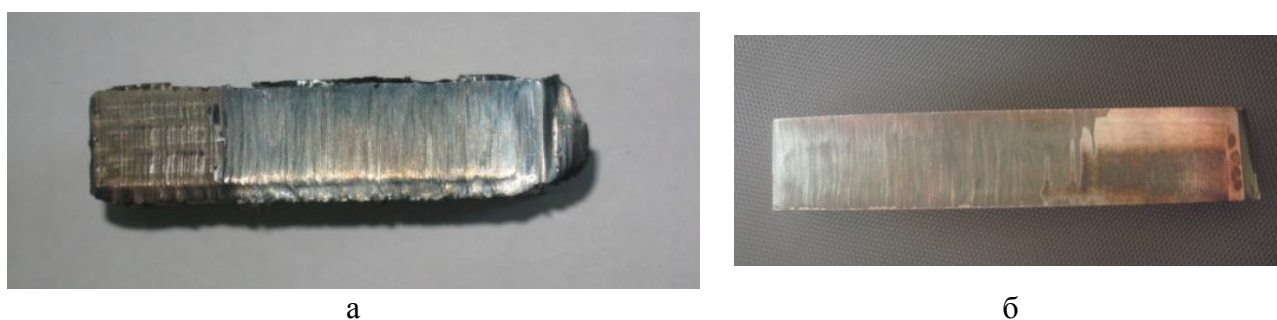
Оброблена поверхня заготовки із сталі 45 з бронзовими стрижнями (а) та послідовні стадії знімання поверхневих шарів після обробки (б)
